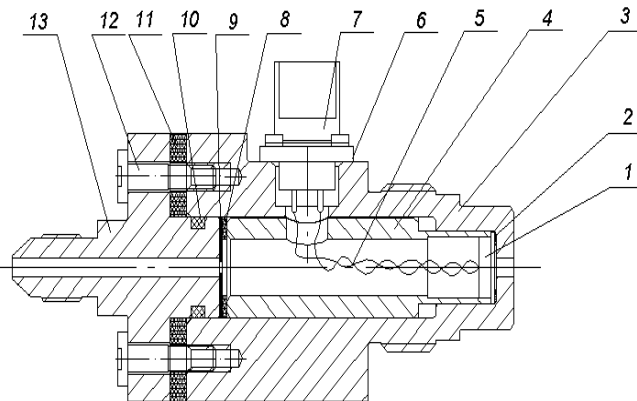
Герметичный корпус с установленным датчиком ДМИ-0.6-1:
